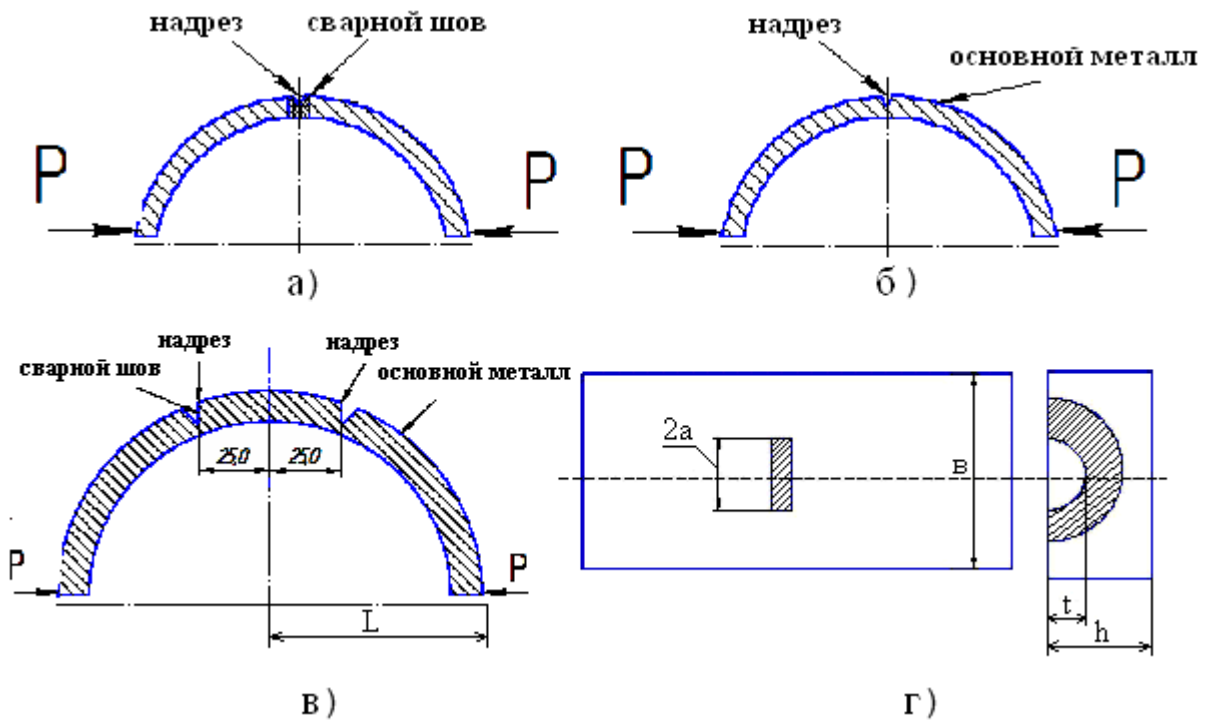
Варианты нанесения надрезов в сварных трубах:
